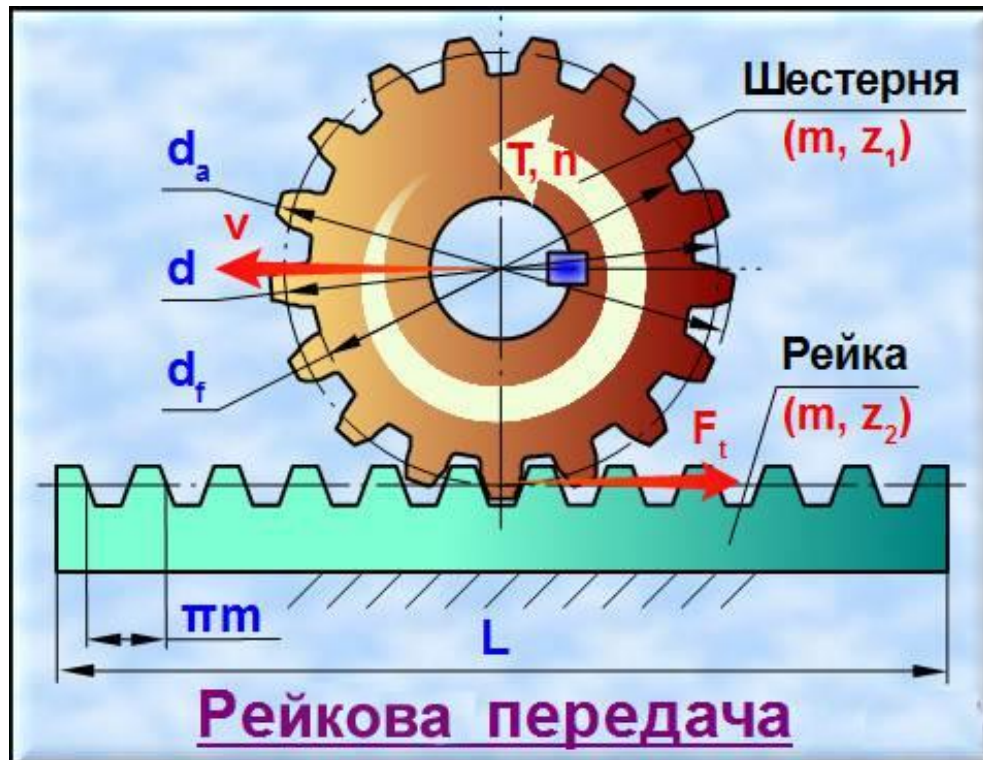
Сили в зачеплення шестерні і зубчастої рейки
